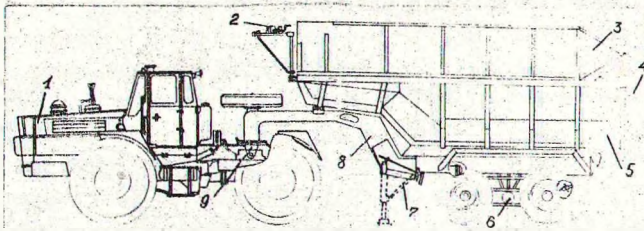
Лесотранспортная машина ЛТ-143: 1-трактор Т-157; 2-устройство для установки запасного колеса; 3-надставные борта; 4-механизм запираения; 5-кузов; 6-тележка; 7-опорно-стояночное устройство; 8-рама; 9-седельно-сцепное устройство.
